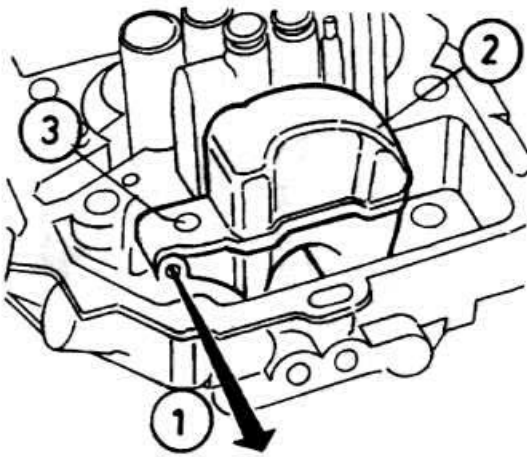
Поплавковое устройство карбюратора, вид со стороны верхней крышки.
